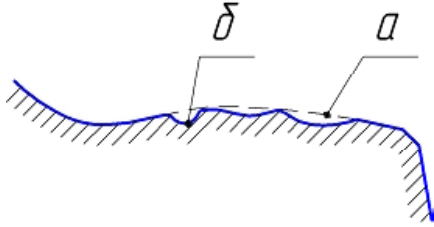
Искажение контура рабочей боковой поверхности зубьев шестерни, возникающие в процессе эксплуатации: *a* – начальный контур, *b* – искаженный контур
